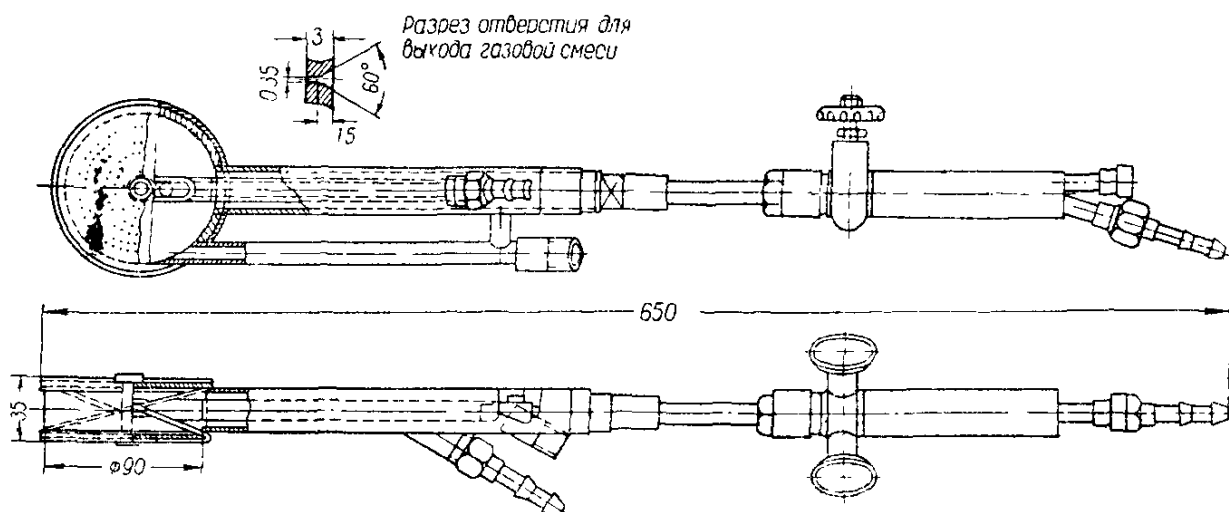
Торцевая газопрессовая сварка:
